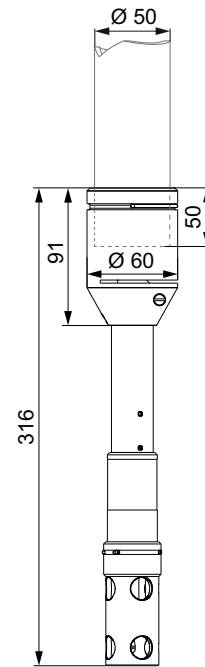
Abmessungen des Sensors mit Halter (Angaben in mm). Das Rohr mit Außendurchmesser 50 mm gehört nicht zum Sensor.
